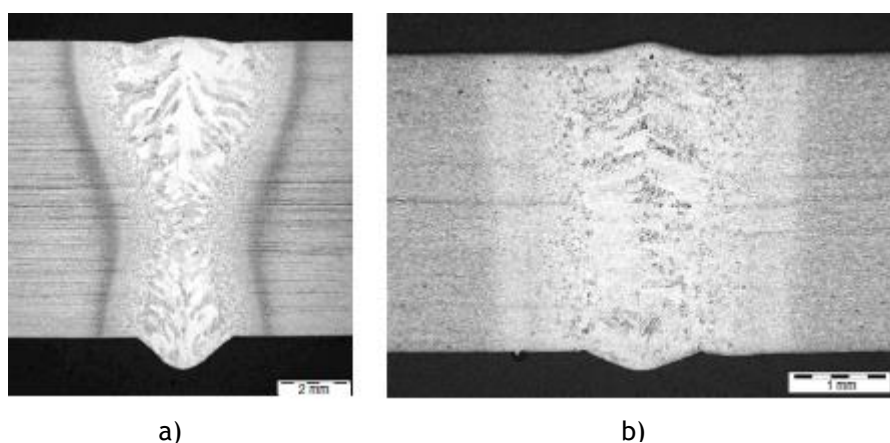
Macroestruturas de soldadura laser *keyhole* em Ti-6Al-4V para diferentes espessuras: a) 9,3 mm; b) 3,2 mm
